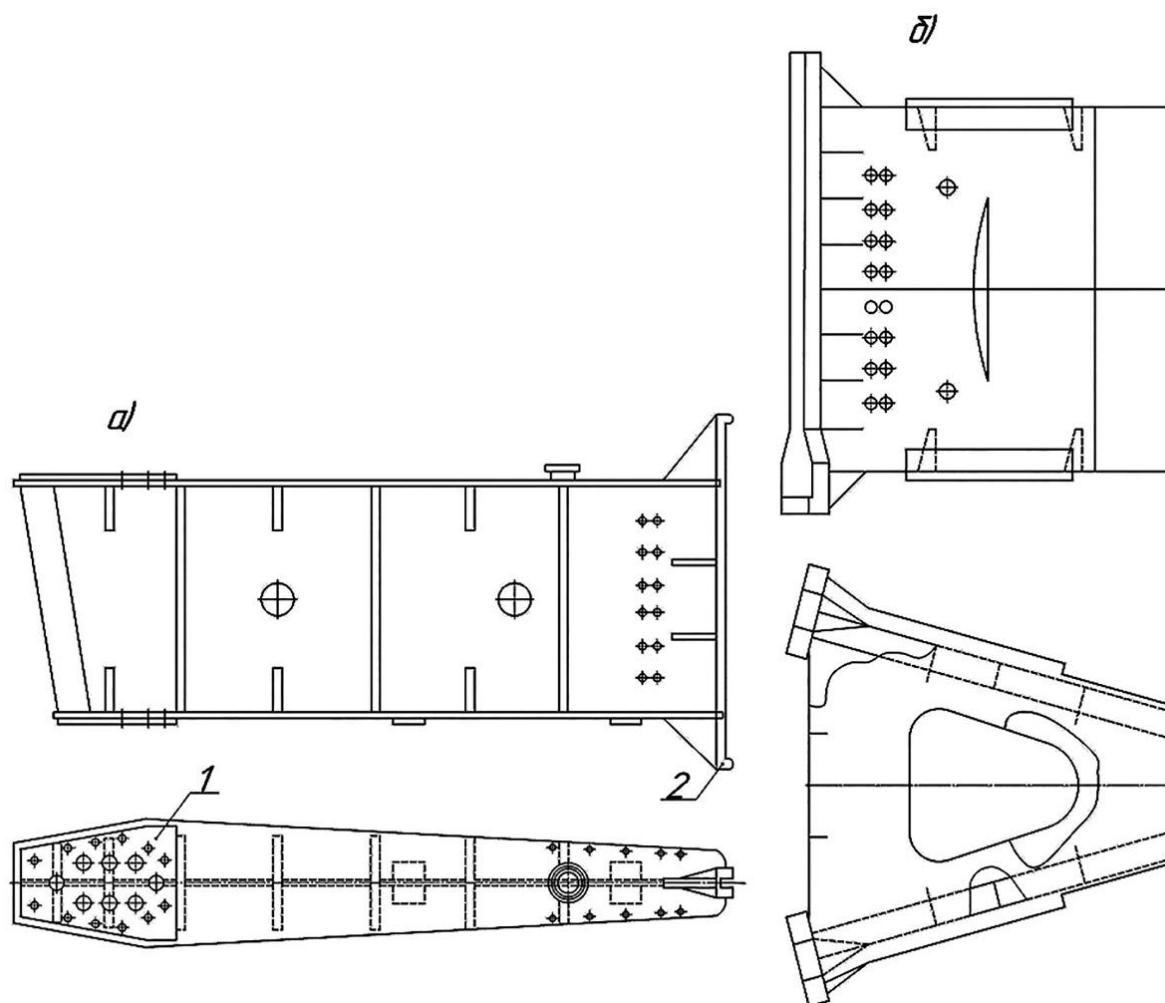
Форми спиць ротора: а) двотаврового перерізу: 1 – накладка, 2 – клинова смуга; б) коробчастого перерізу
